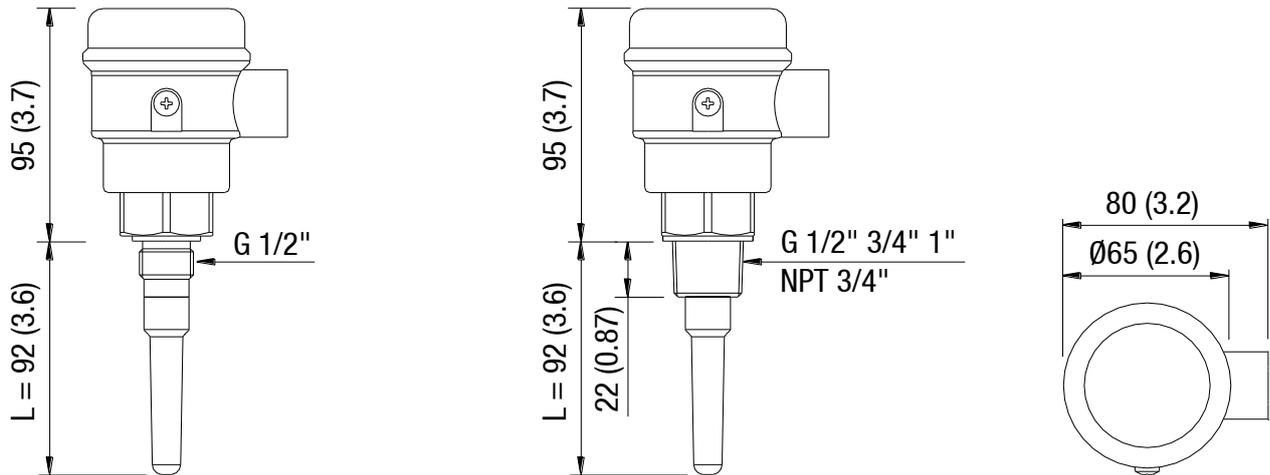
Abmessungen CN 7120, Gehäuse Ø 65 mm
